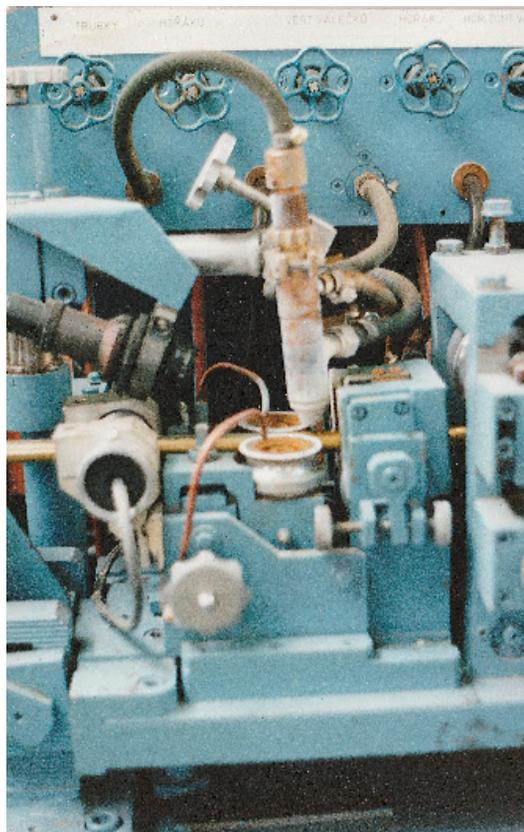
Узел сварки (камера вытяжки газов снята) стана АДСТ 5...25-1К левого исполнения, датчик теплового потока (слева), над ним — оптический прибор для вывода изображения зоны сварки на экран дисплея
